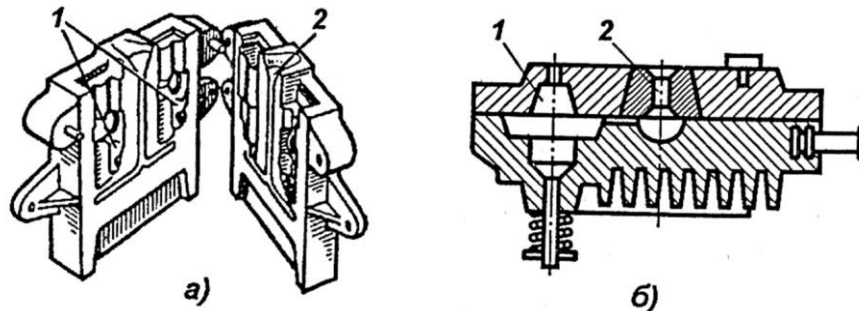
Конструктивные формы кокилей: а – с вертикальным разъемом; б – с горизонтальным разъемом; 1 – форма гнезда для отливки детали; 2 – литниковая система
